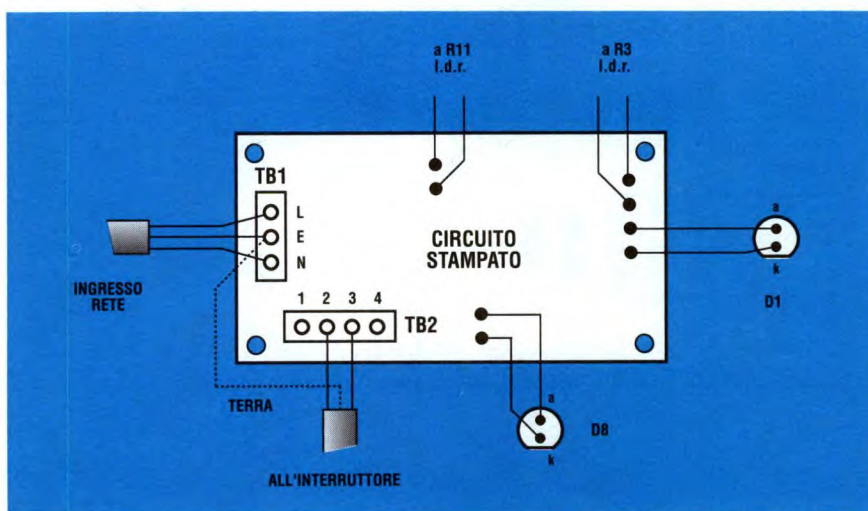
Cablaggio fra il circuito stampato e i componenti esterni.
